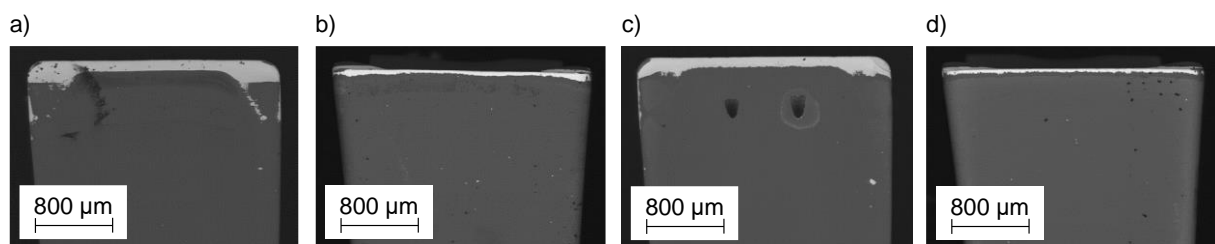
Werkzeugschneiden nach Erreichen des Abbruchkriteriums bei der Bearbeitung von Ti6Al4V; a) Spanfläche des Referenzwerkzeuges, b) Freifläche des Referenzwerkzeuges; c) Spanfläche des microCutOff-Werkzeuges, d) Freifläche des Referenzwerkzeuges
